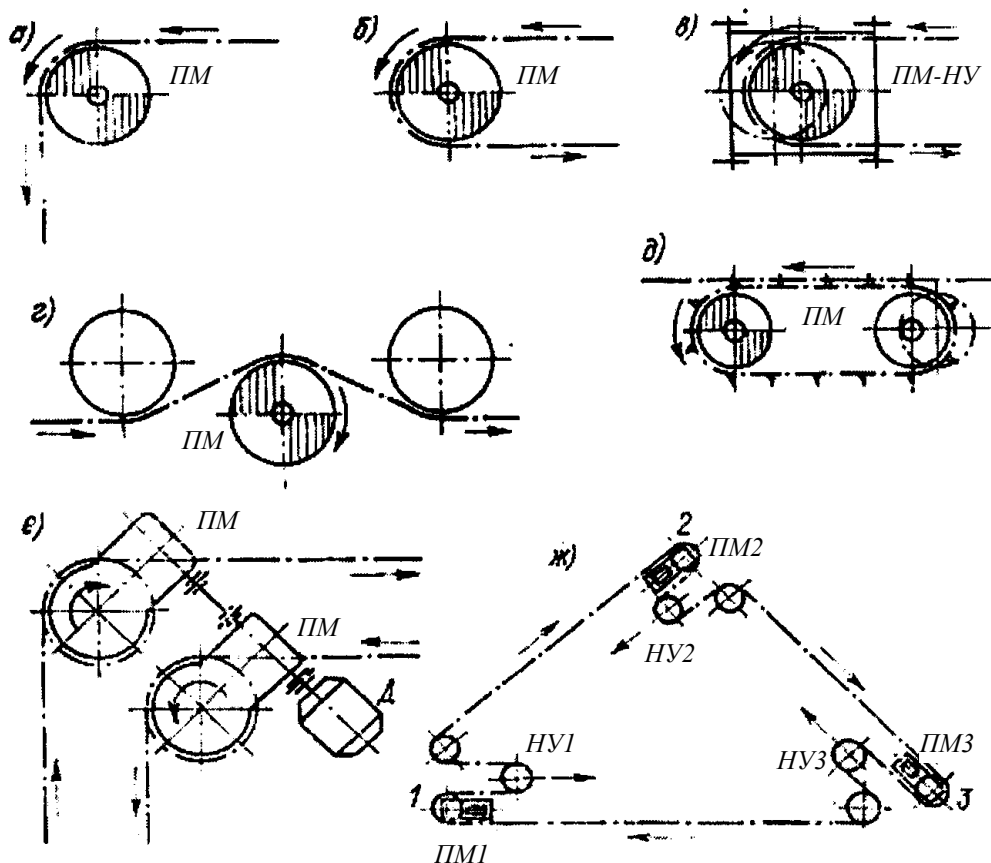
Приводы: а-г – угловые с различными углами поворота; д – прямолинейный; е – объединенный; ж – многодвигательный; ПМ – приводной механизм; Д – электродвигатель; НУ – натяжное устройство
